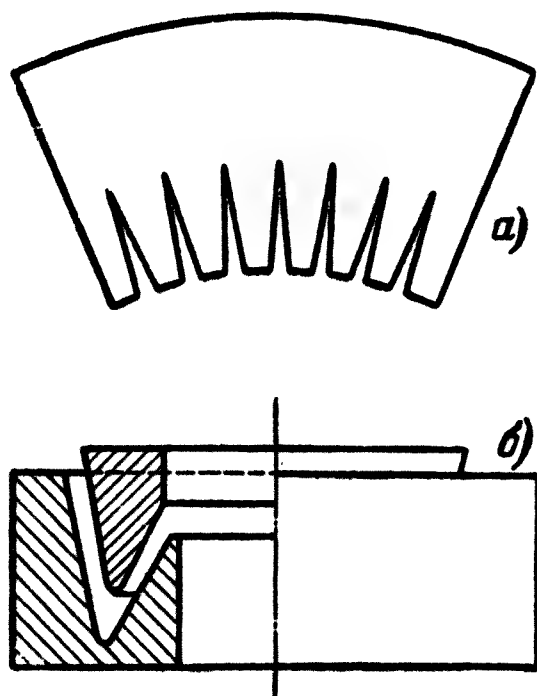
Прессформа и заготовка для максимального конуса.
